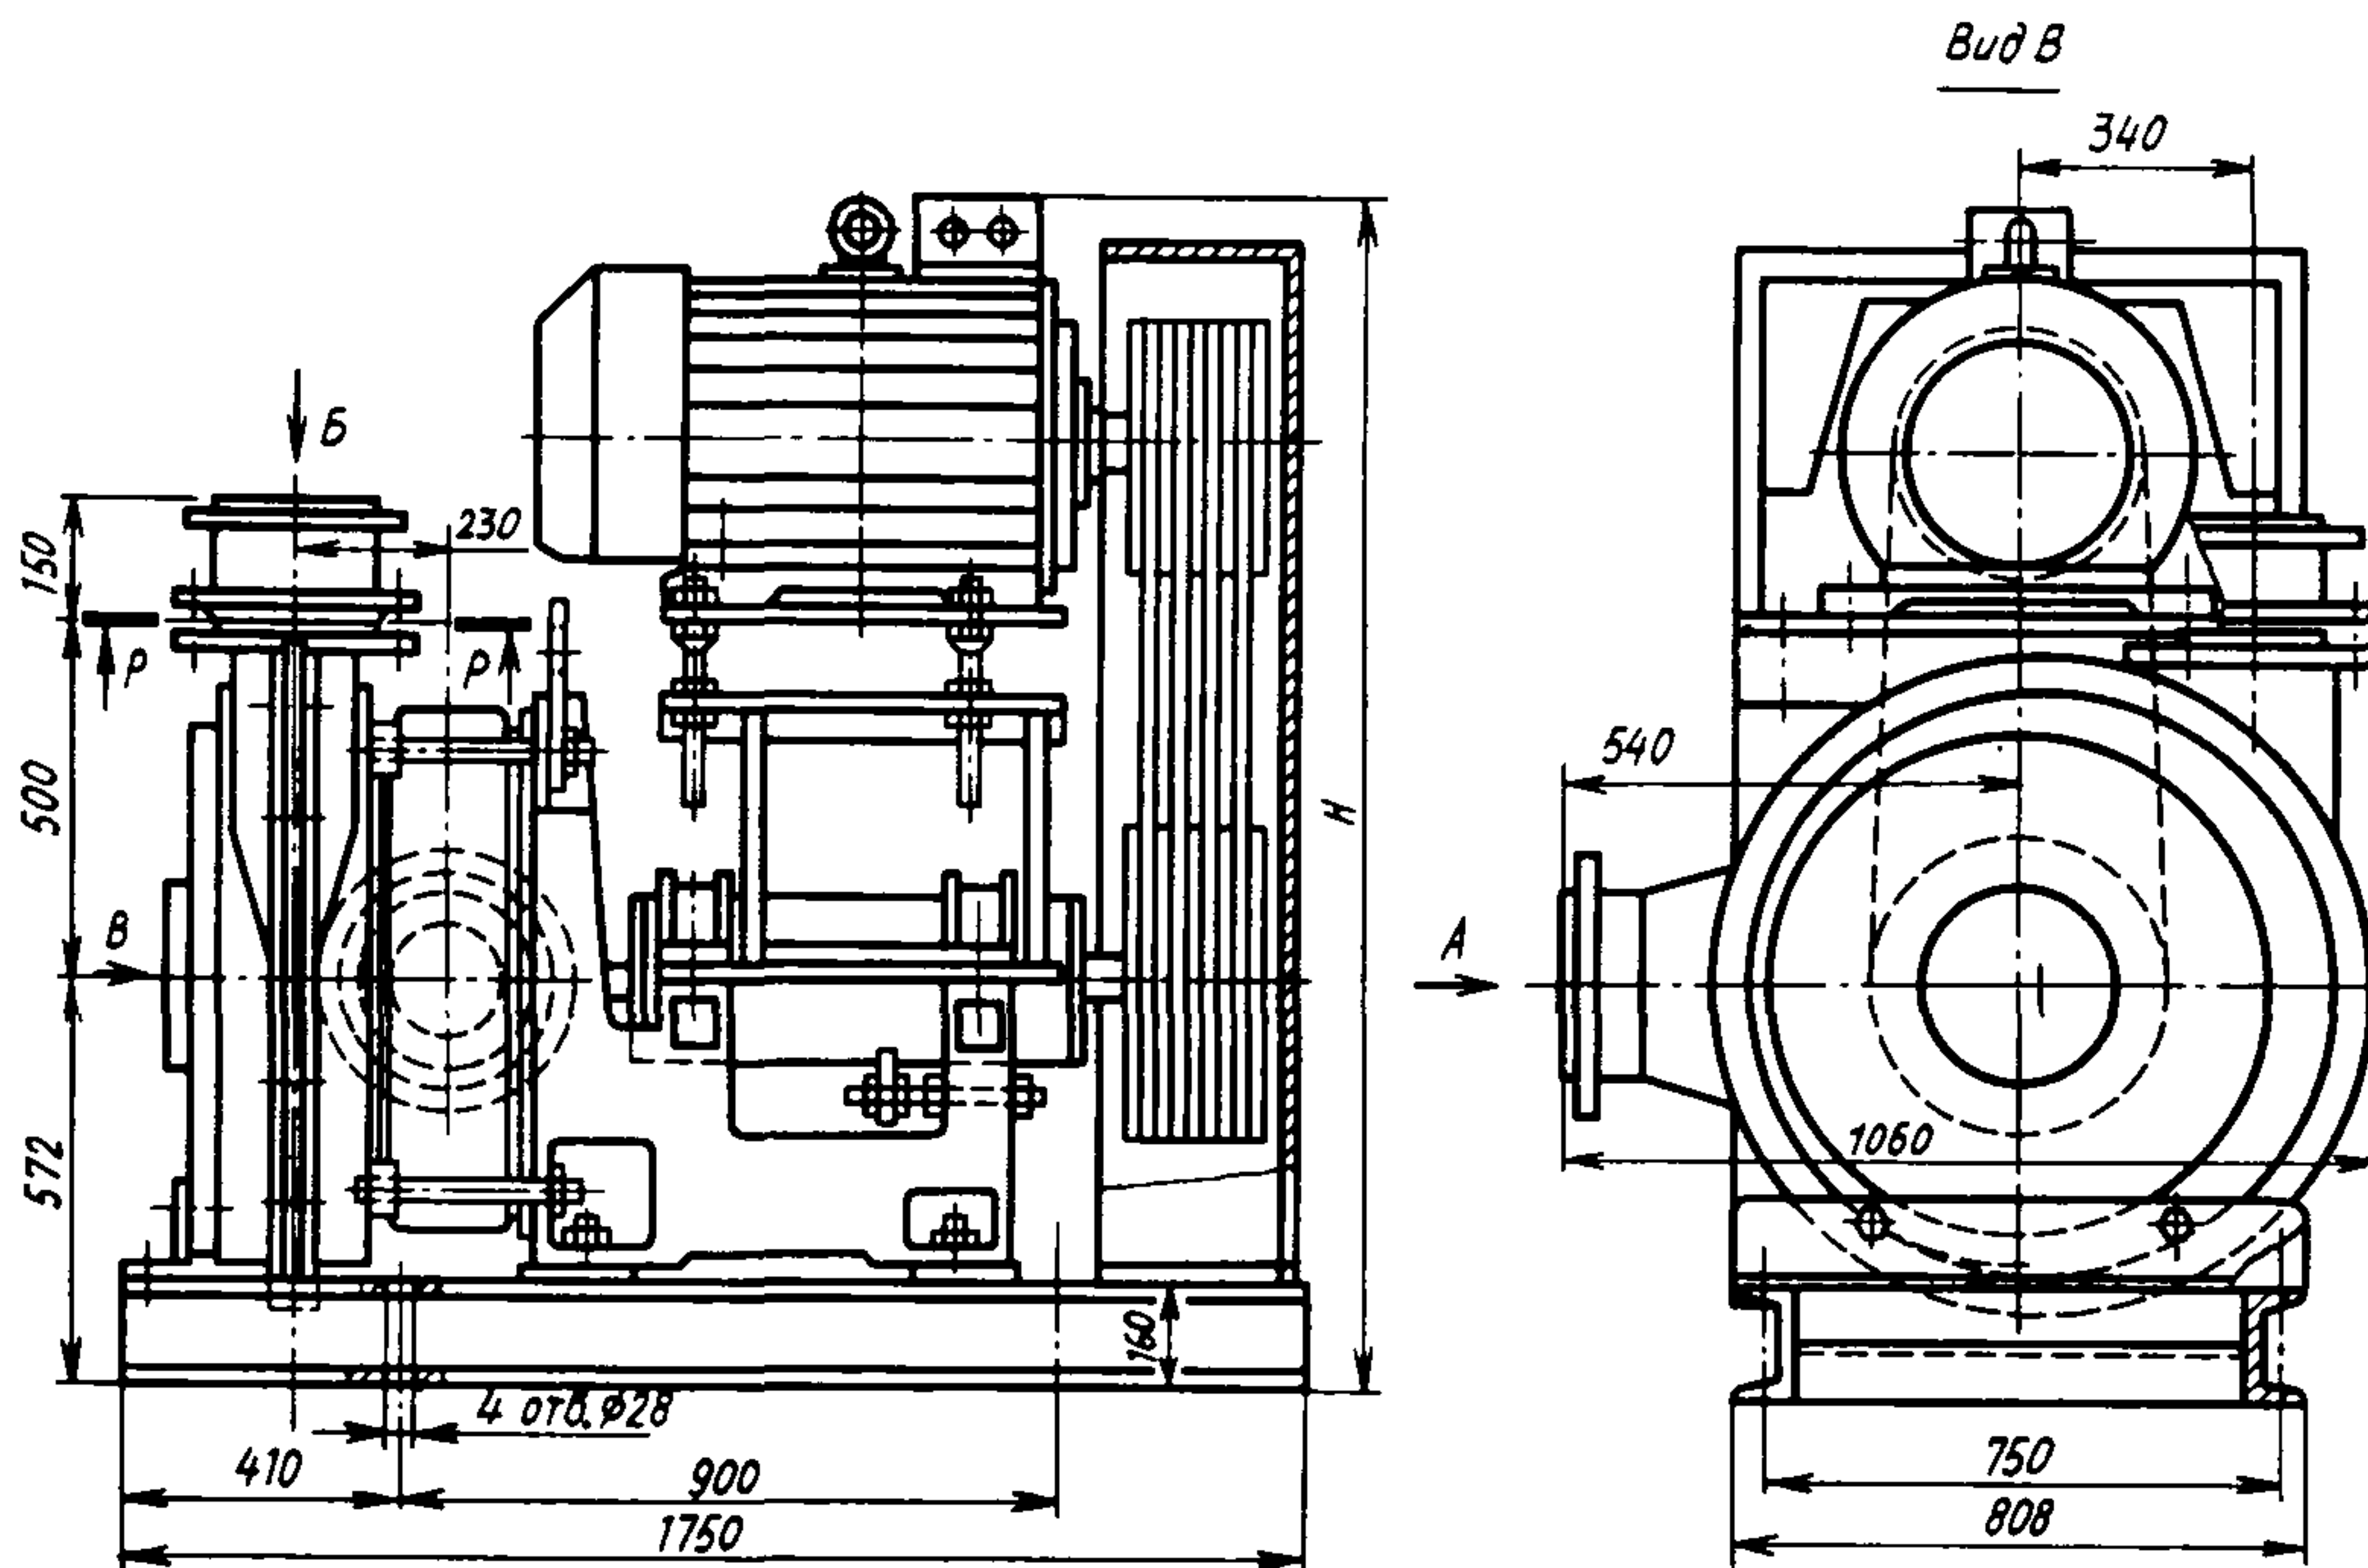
Габаритный чертеж электронасосных агрегатов типа НПБР с приводом через клиноременную передачу
